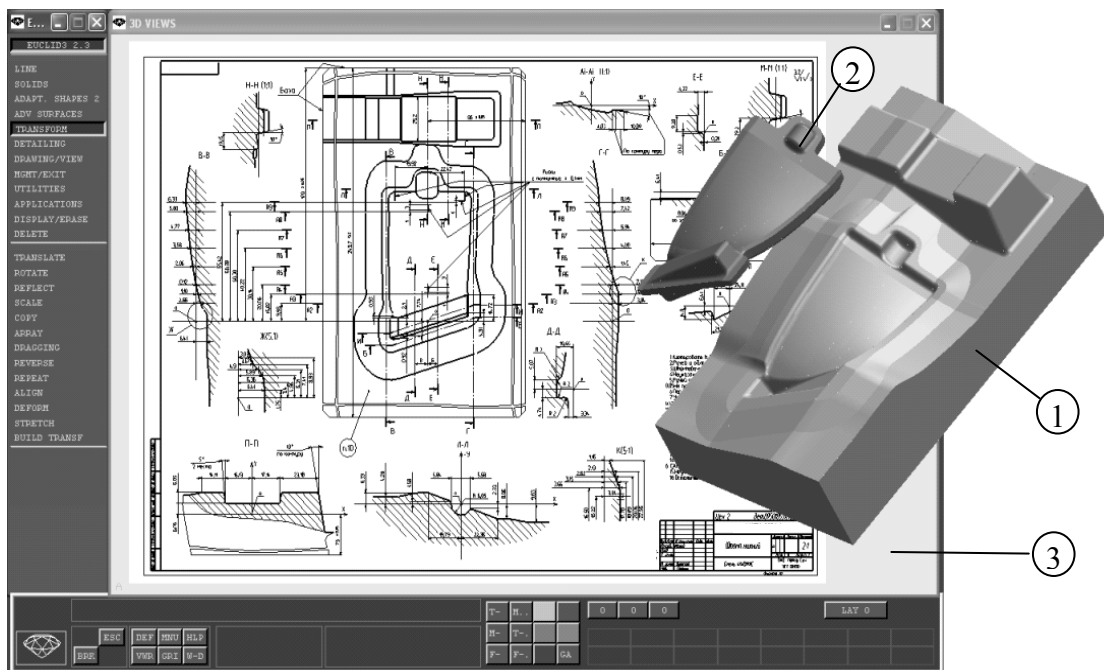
Точная объемная штамповка лопатки компрессора: 1 – аналитический эталон формообразующей вставки ковочного штампа; 2 – аналитический эталон поковки; 3 – чертеж формообразующей вставки ковочного штампа.
